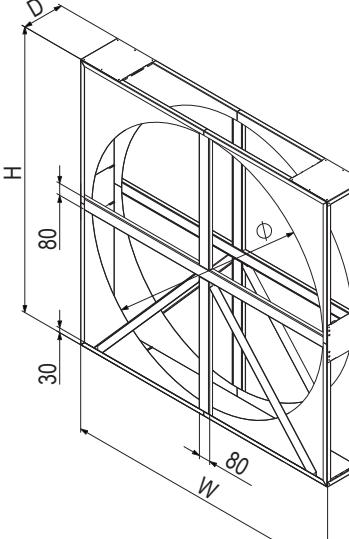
Massblatt für SM Gehäuse (Abmessungen in mm)
